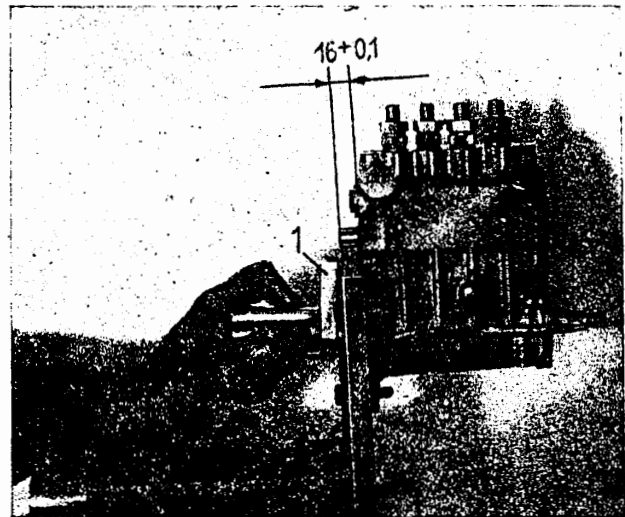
Abstand zwischen Flanschflächen und Einstellvorrichtung (Werkzeug Nr. W 212) prüfen (1)
